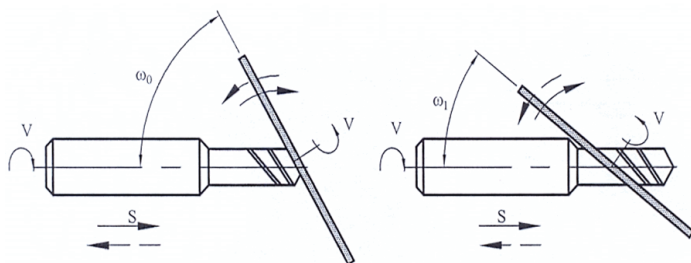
Схема изменения ориентации осей заготовки сверла и шлифовального круга методом поворота оси шлифовального шпинделя.
